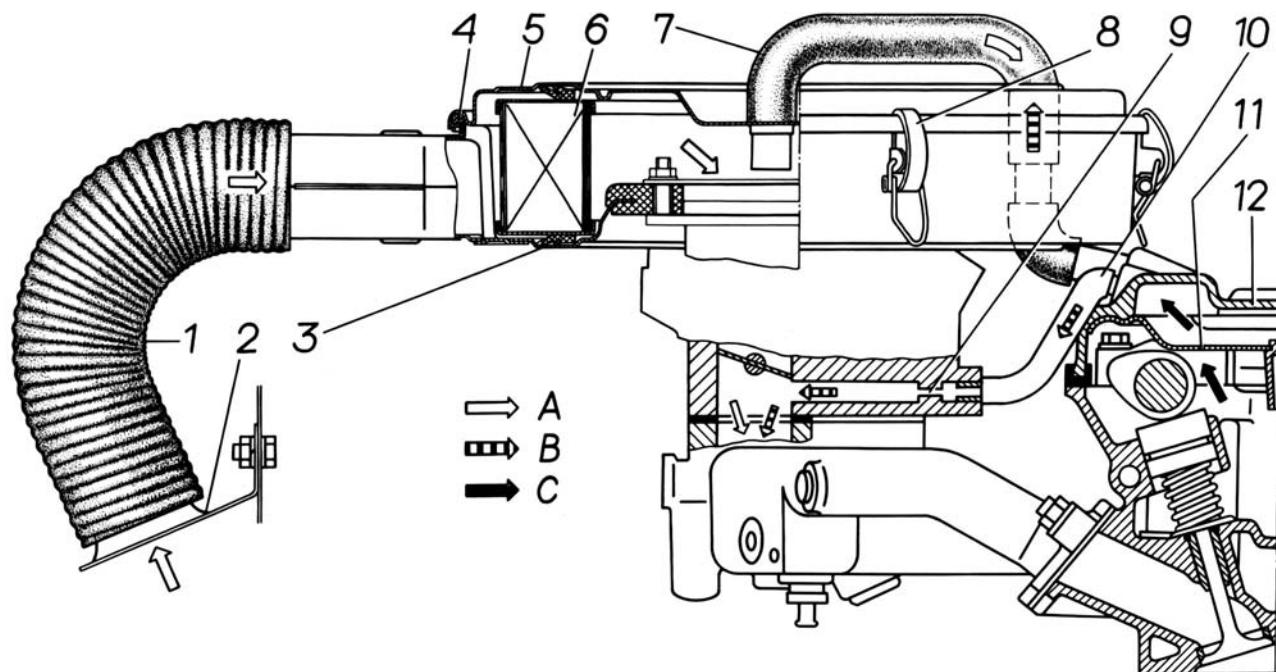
Схема системы вентиляции картера двигателя: А - чистый воздух; В - смесь чистом воздуха с картерными газами; С - картерные газы; 1 - воздухозаборный шланг; 2 - воздухозаборный патрубок; 3 - корпус воздушного фильтра; 4 - уплотнительная прокладка; 5 - крышка воздушного фильтра; 6 - фильтрующий элемент; 7 и 10- шланги; 8 - защелка; 9 - калиброванное отверстие в корпусе дроссельных заслонок карбюратора; 11 - маслоотделитель; 12 - крышка клапанов
